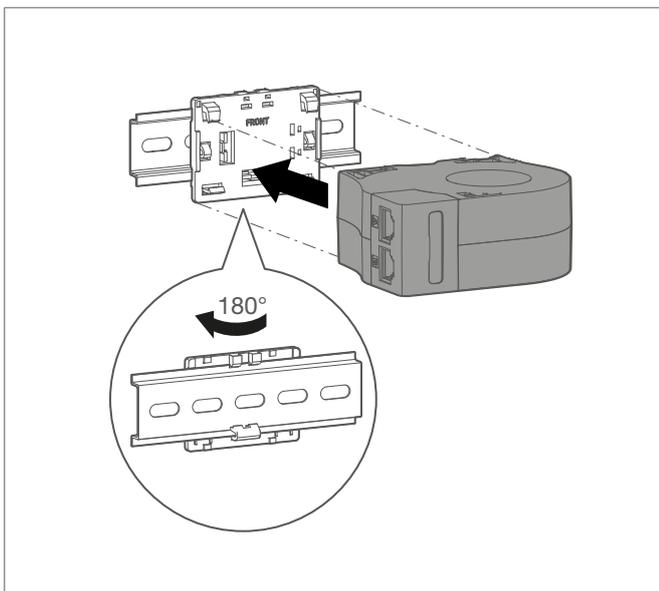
HR72x - Orientation de montage sur rail DIN vertical
